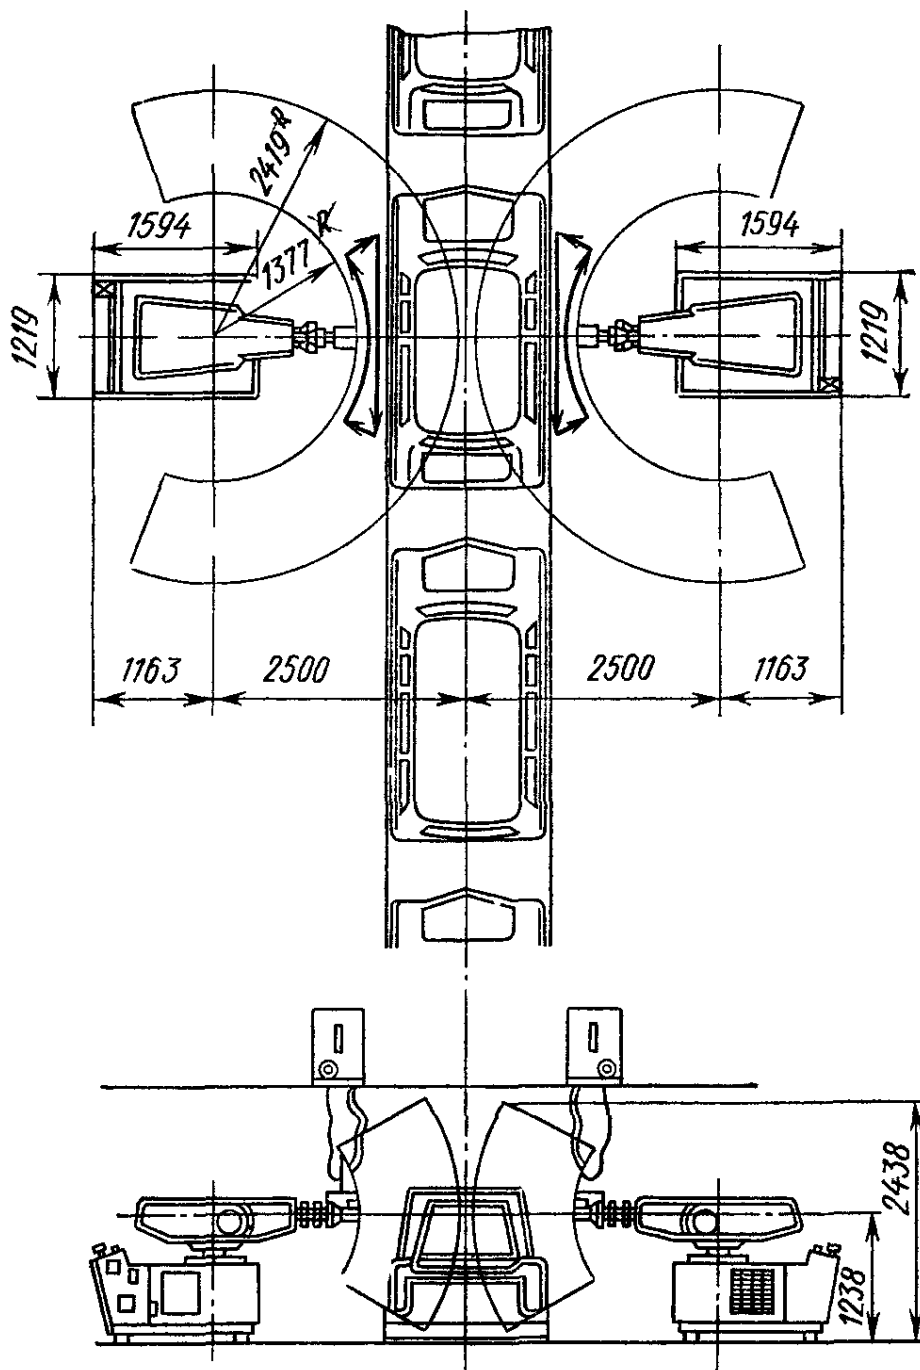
Схема расположения роботов при точечной сварке правой и левой сторон кузова автомобиля
